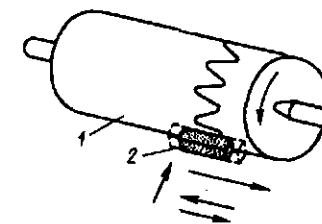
Схема рабочих движений инструмента и обрабатываемой детали при суперфинишировании: 1 – деталь; 2 – абразивный брусок
